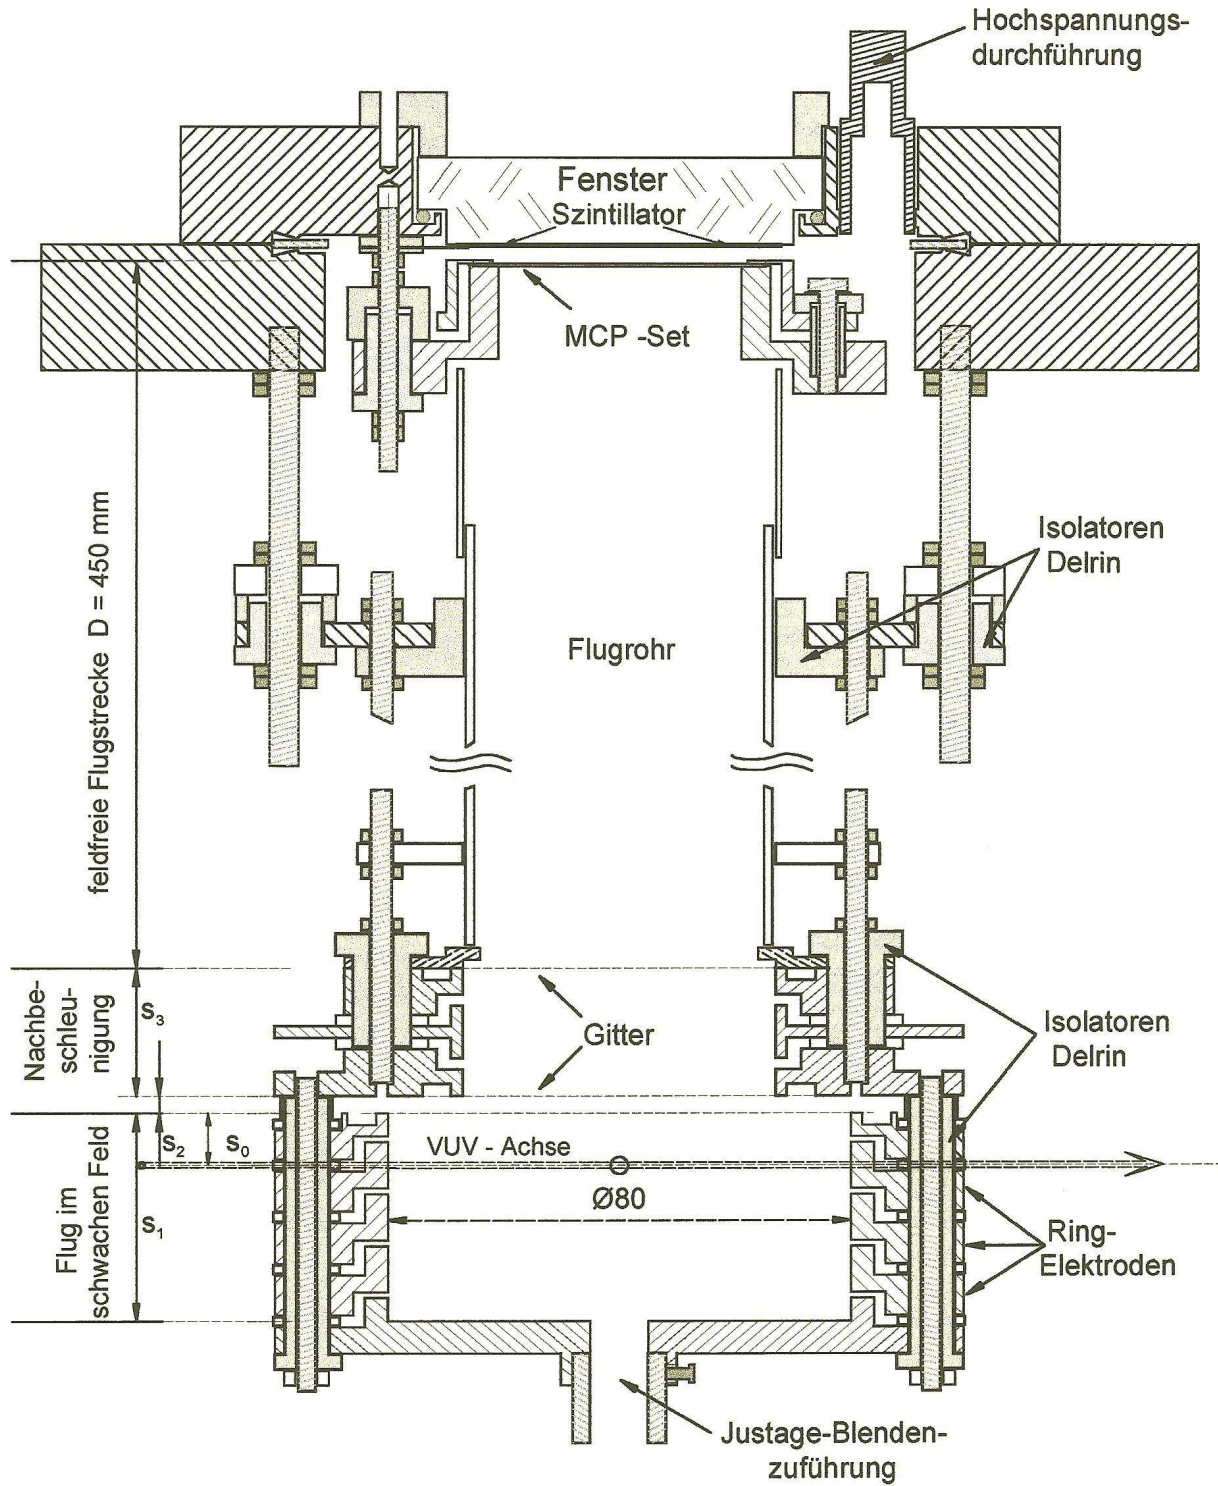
Explosionszeichnung MCP- Detektorkopf
